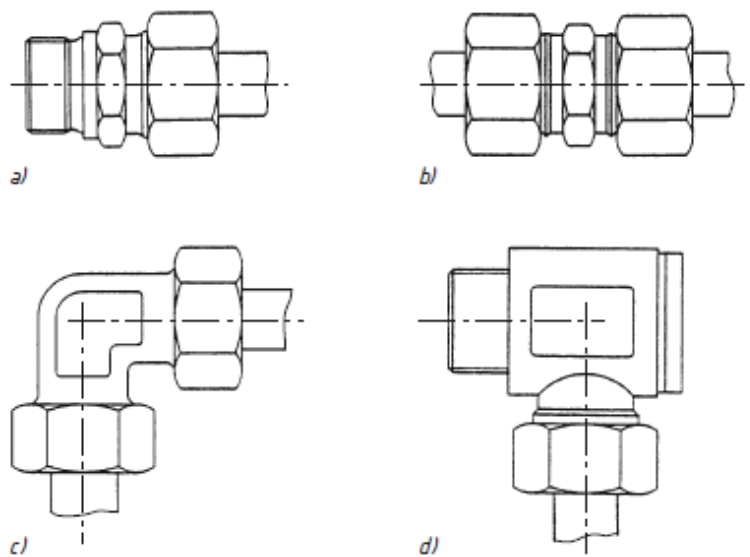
Rohrverschraubungen nach ISO 8434 für Hydraulikanlagen (Rohraußendurchmesser 6 bis 38 mm, bis PN 630). a) Schneidring, Dichtkegel 24° (DIN 2353), b) Bördel, Dichtkegel 37°, c) flachdichtend mit O-Ring (Bördel oder Endstück 90°), d) Schweiß-(Dicht-)Kegel 24° mit O-Ring (DIN 3865)
